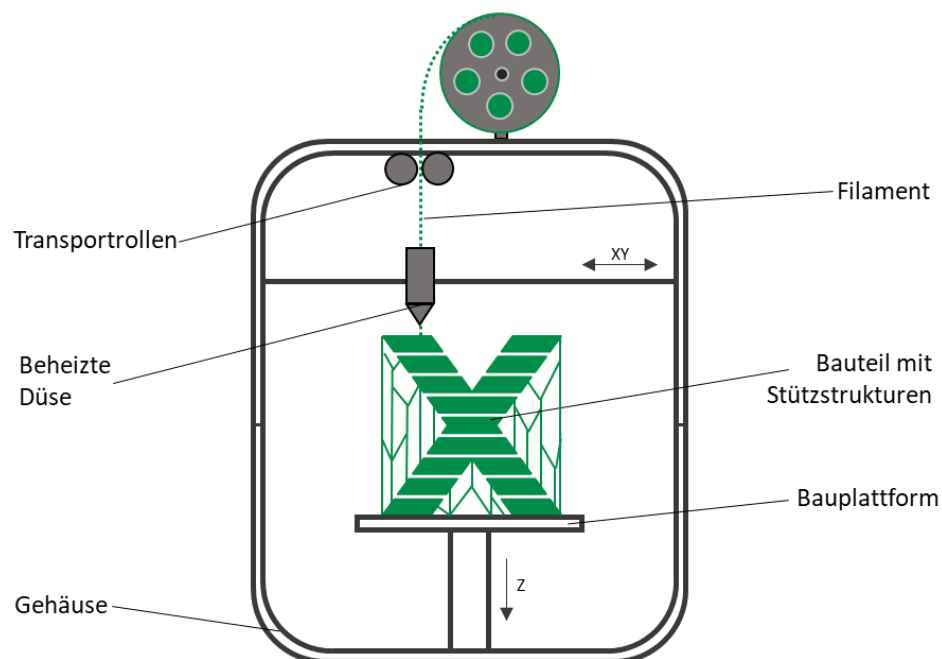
Schemazeichnung des Fused Layer Manufacturing. In Anlehnung an: [Bre-13, Hag-14].
